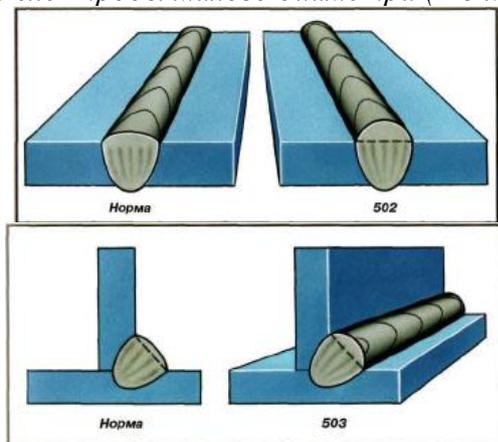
Выпуклость сварного шва (Код дефекта: 502; 503)
